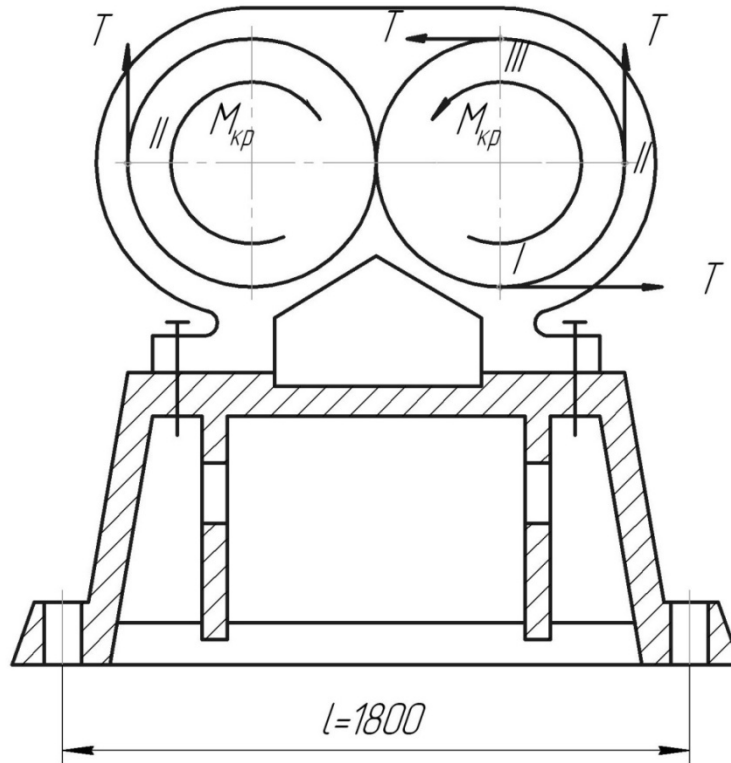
Схема навантаження фундаментної плити пластозмішувача
